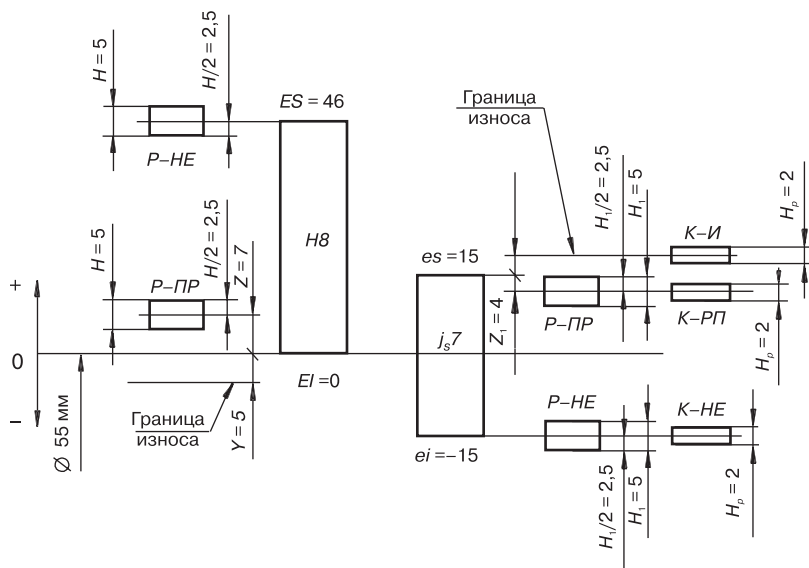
Схемы полей допусков калибров для контроля деталей соединения $\varnothing 55 H8/j_7$
